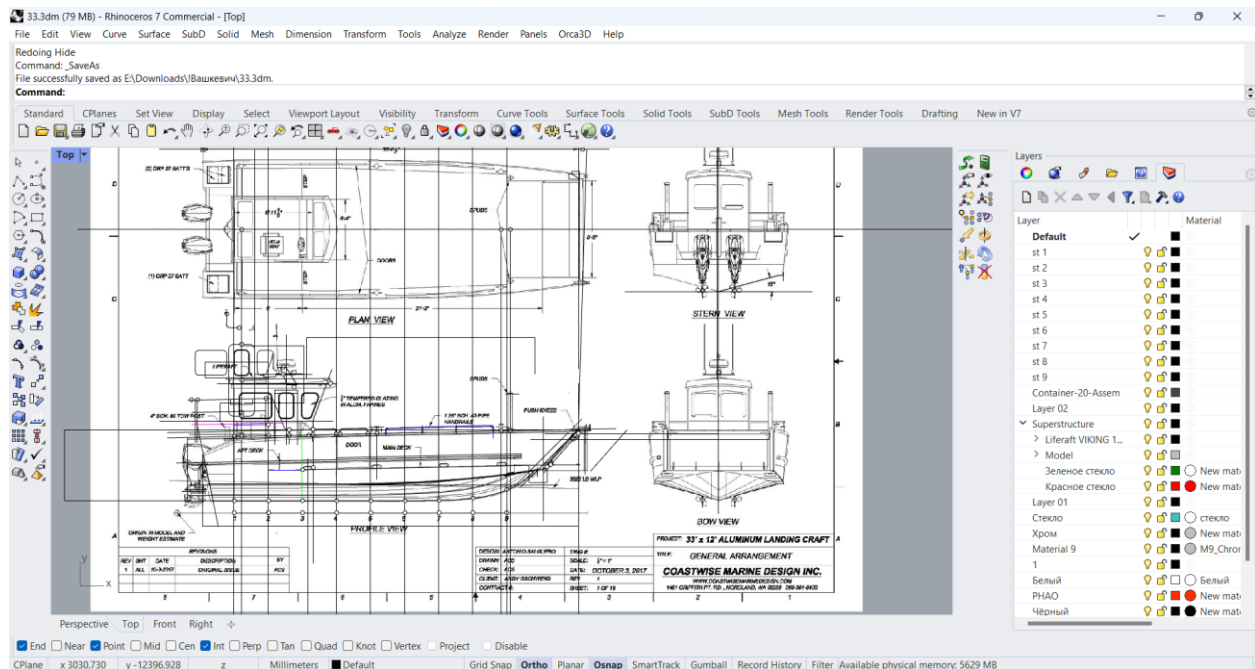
Процес оцифрування корпусу судна-прототипу
